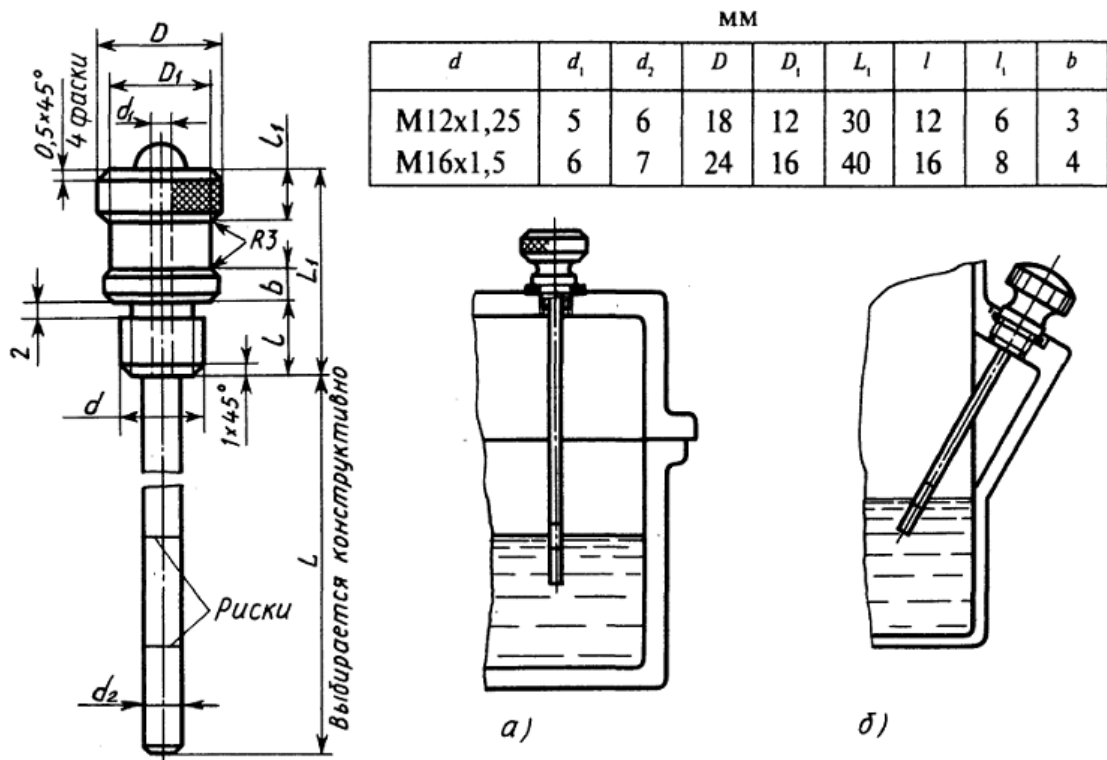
Жезловый маслоуказатель и способы его установки на корпусе:
